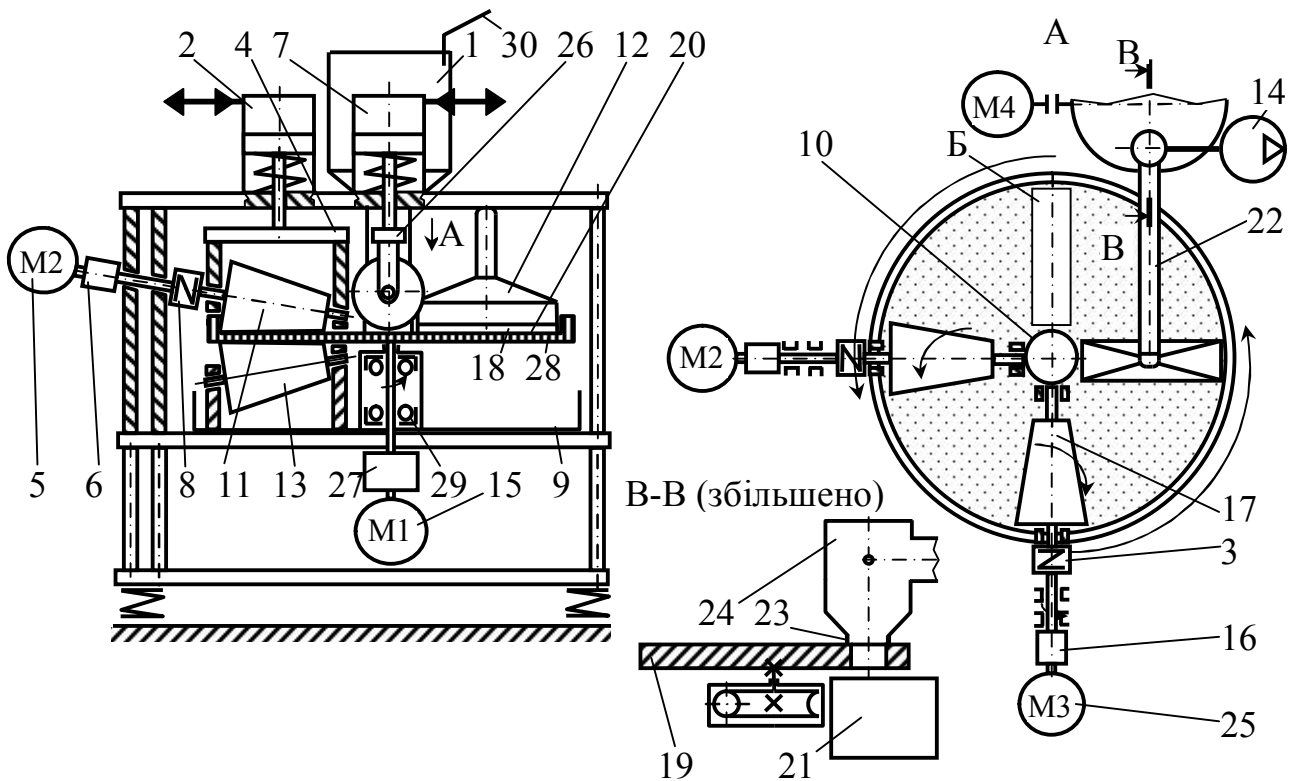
Схема гідроімпульсної вальцьової установки для остаточного потокового віброударного зневоднення харчових відходів: 1 – бункер; 2, 7 – гідроциліндри ГП; 3, 8 – пружні муфти; 4, 26 – траверси; 5, 15, 25 – електродвигуни; 6, 16, 27 – планетарні редуктори; 9, 21 – баки; 10 – гумовий екран; 11, 13, 17 – конічні вальці; 12 – патрубок; 14 – вакуумний насос; 18 – гумовий ніж; 19 – диск; 20 – фільтрувальна сітка; 22 – труба; 23 – ущільнення; 24 – камера; 28 – матриця; 29 – підшипники; 30 – лоток.
